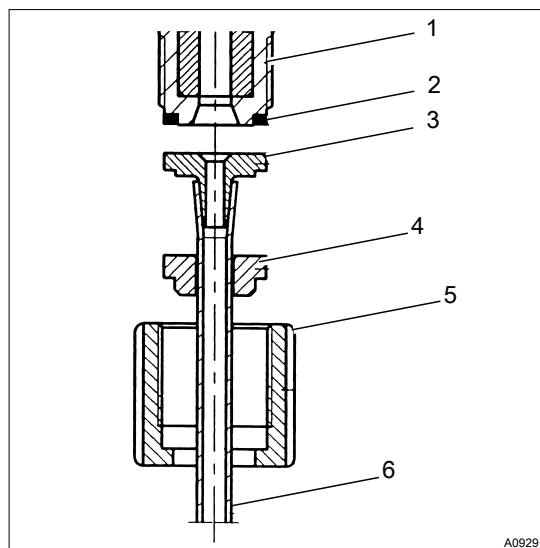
Schlauch mit dem Anschluss-Set anschließen
